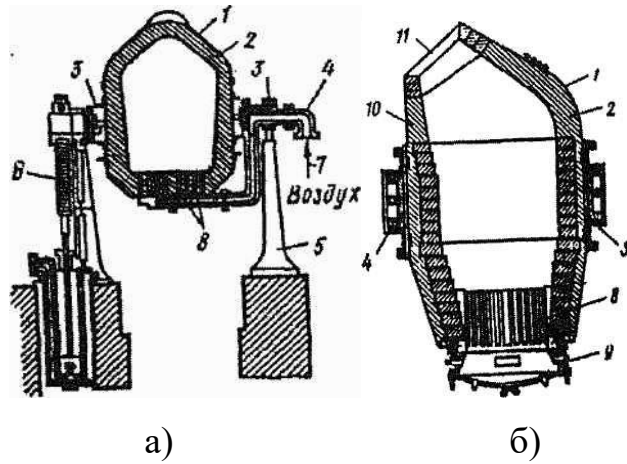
Конверторы. Схема устройства: а – общий вид;
